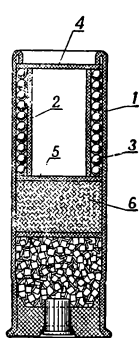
Короткобойный патрон Н. А. Дементьева:
